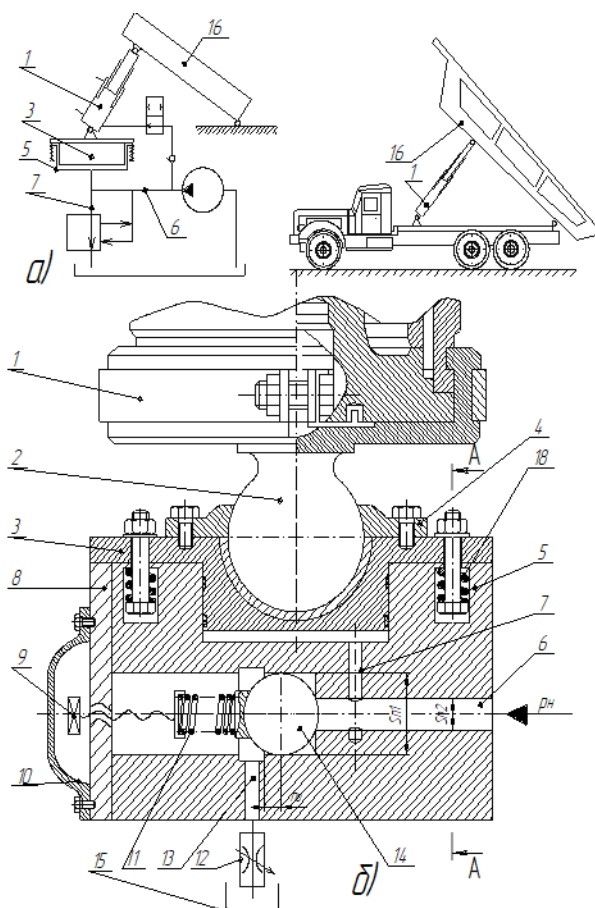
Гідроімпульсний привод віброударного пристрою автомобіля-самоскида: а) – схематичне розташування вузлів привода; б) – конструктивна схема вбудованого клапана-пульсатора
